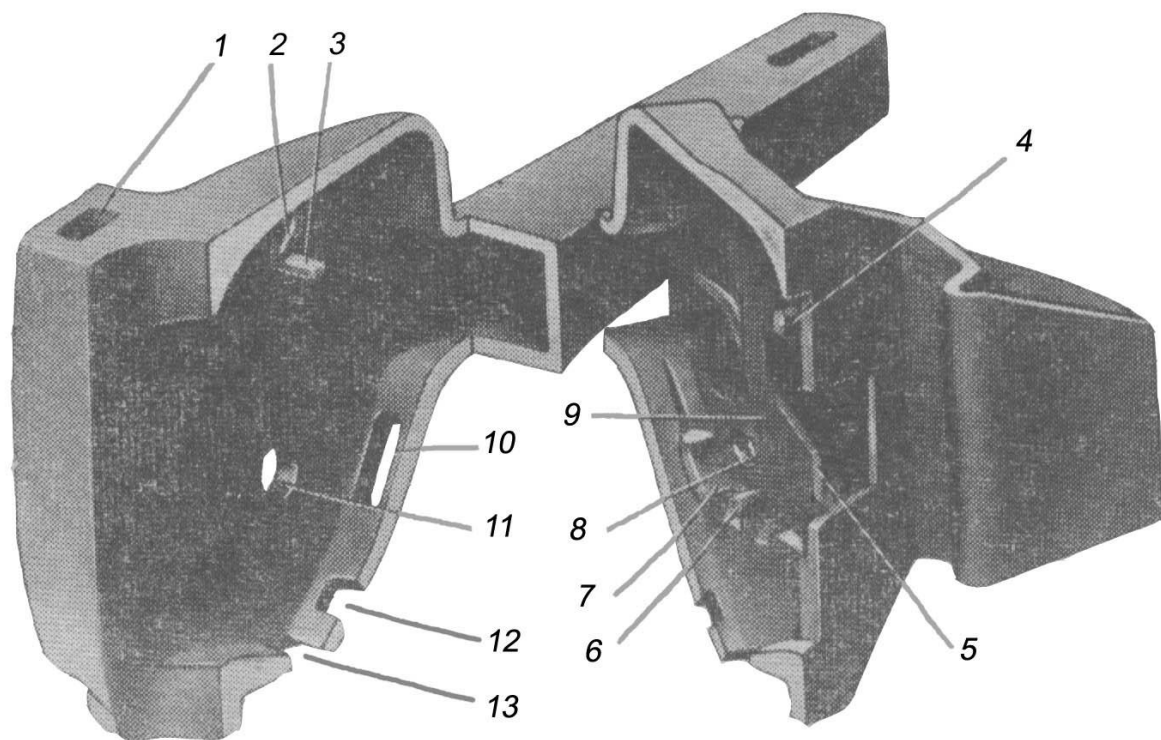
Внутрішня частина корпусу автозчепу СА-3
